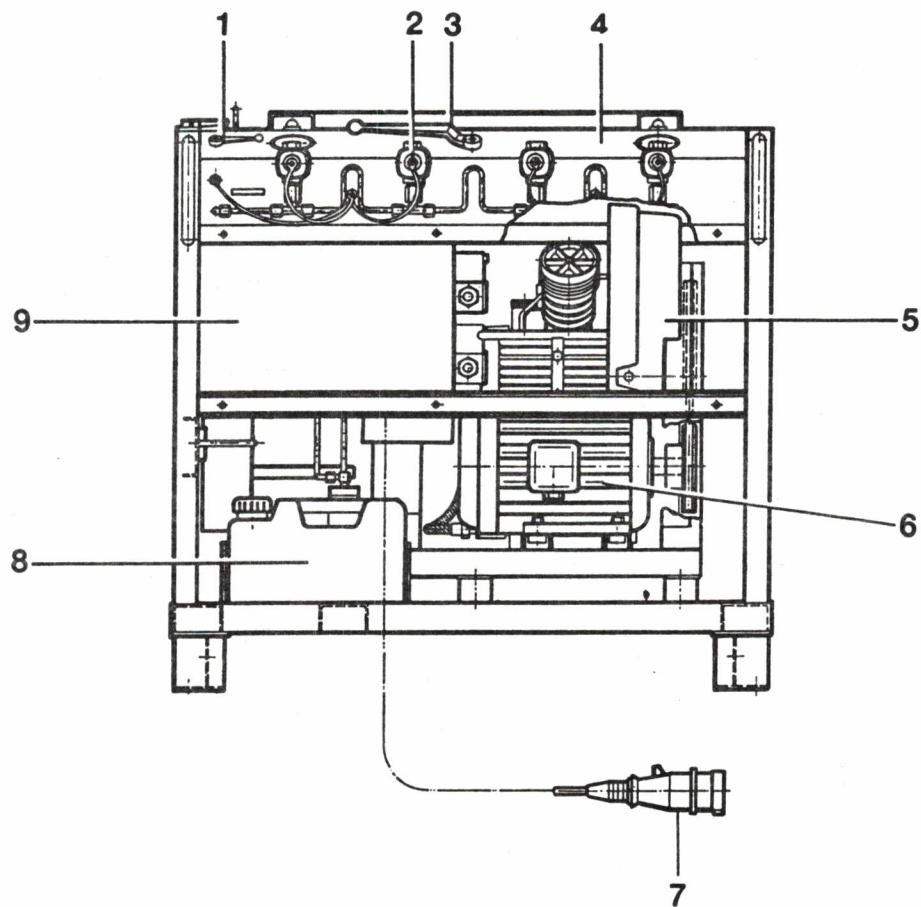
Drucklufterzeuger (EliMot), Seitenansicht, rechts
